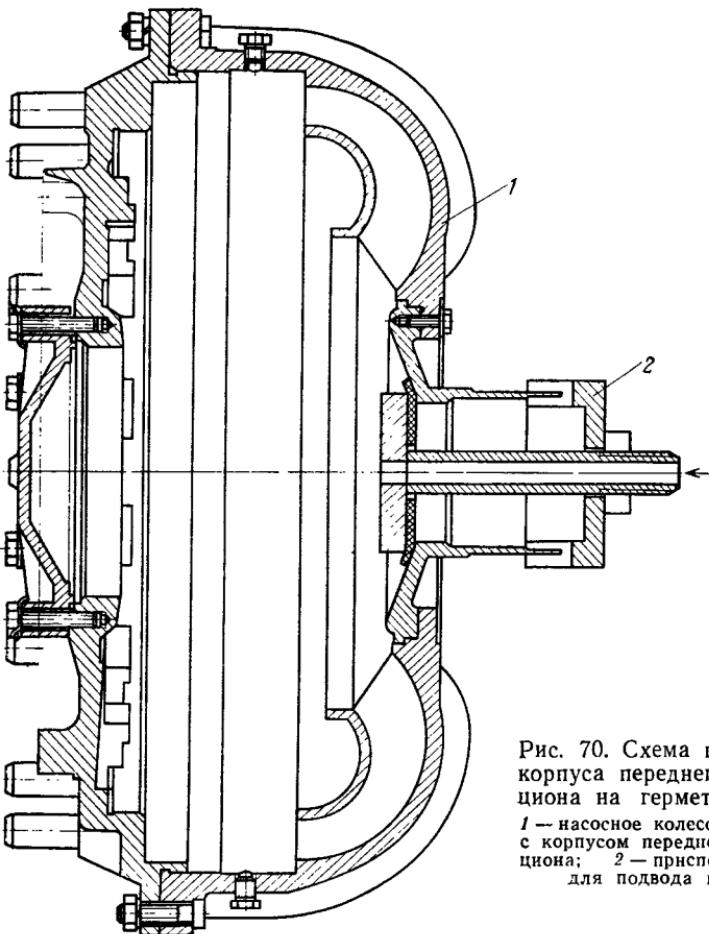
Схема проверки корпуса переднего фрикционa на герметичность:
